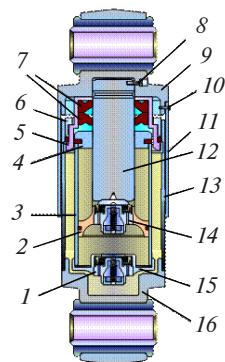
Устройство гидравлического гасителя колебаний:
